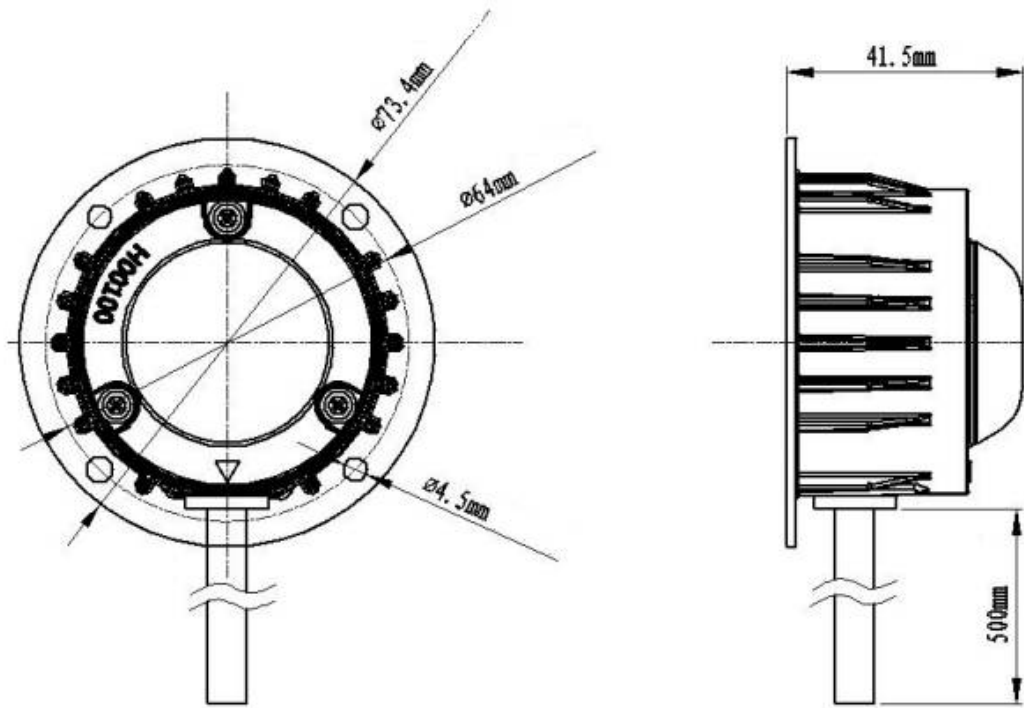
Внешний вид и габаритные размеры светоизлучающего модуля ДБАП02.
